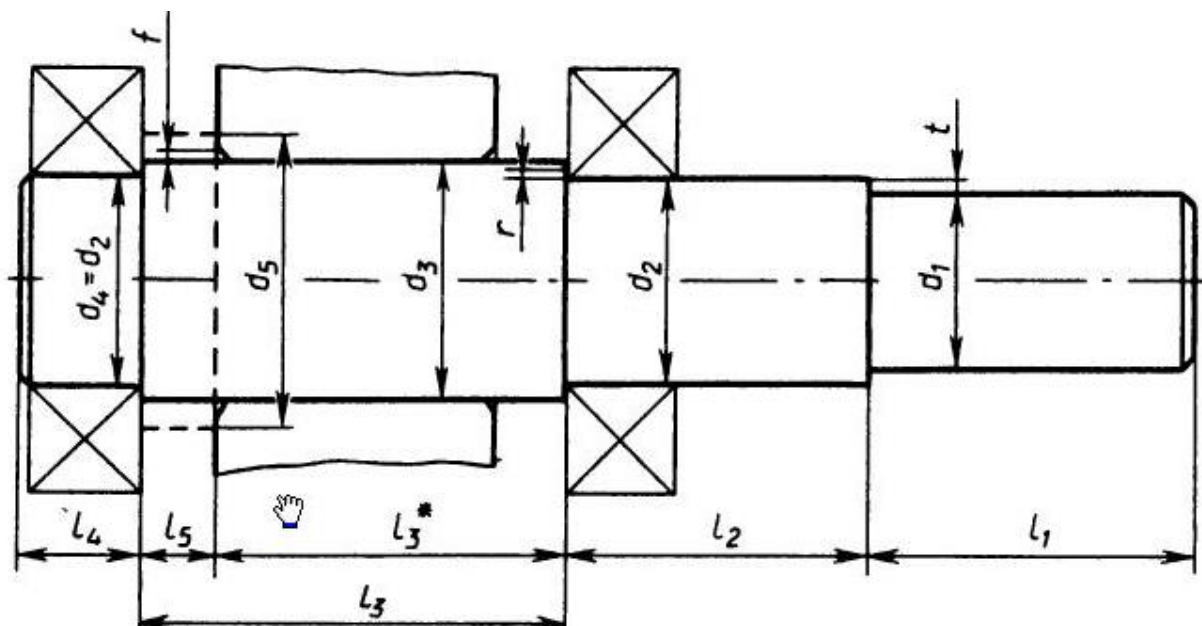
Схема ведомого (тихоходного) вала (вал колеса)
